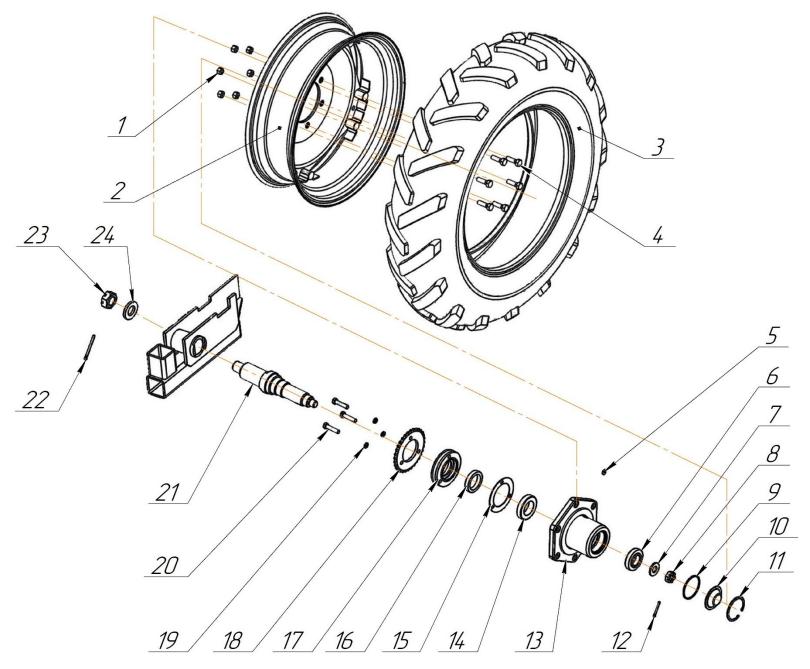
Колесо опорно-приводное и ступица СЗМ 00.2000-01 в сборе
